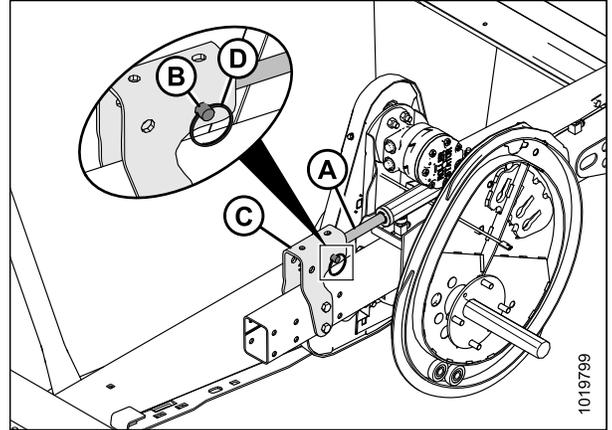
Центральный рычаг мотовила в заднем положении
